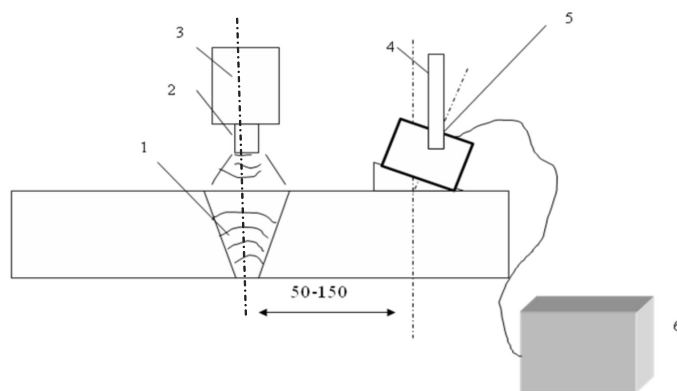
Схема воздействия ультразвука на сварное соединение в процессе сварки: 1 – сварное соединение; 2 – электрод; 3 – держатель; 4 – кронштейн; 5 – ультразвуковой преобразователь; 6 – ультразвуковой генератор
